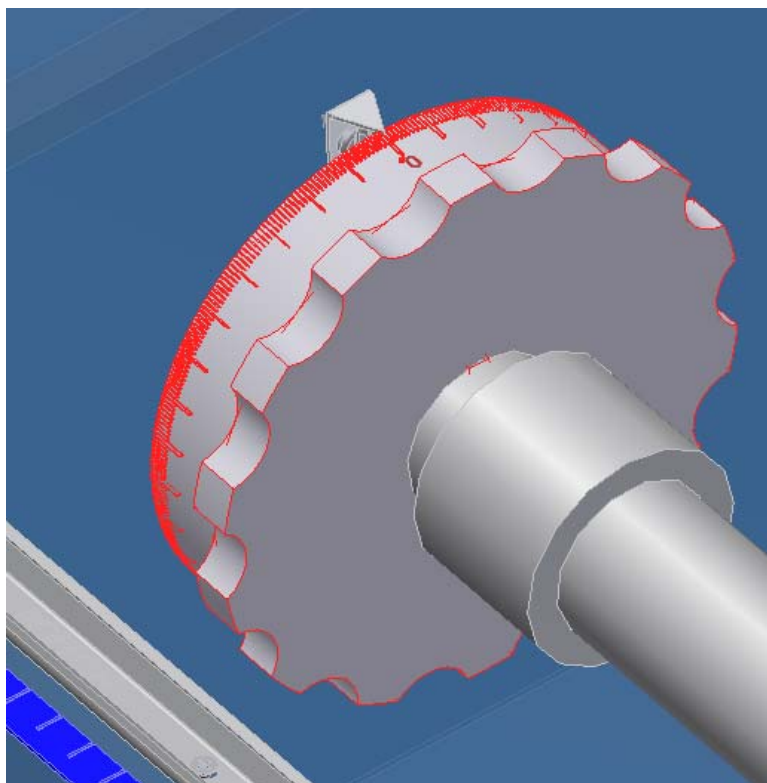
Uložení vačkové hřídele v přípravku – hřídel kreslena zjednodušeně
